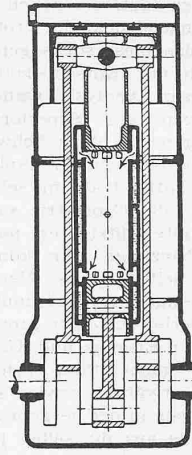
Gegenkolbenmotor mit oberem Querhaupt, Lizenz Junkers
